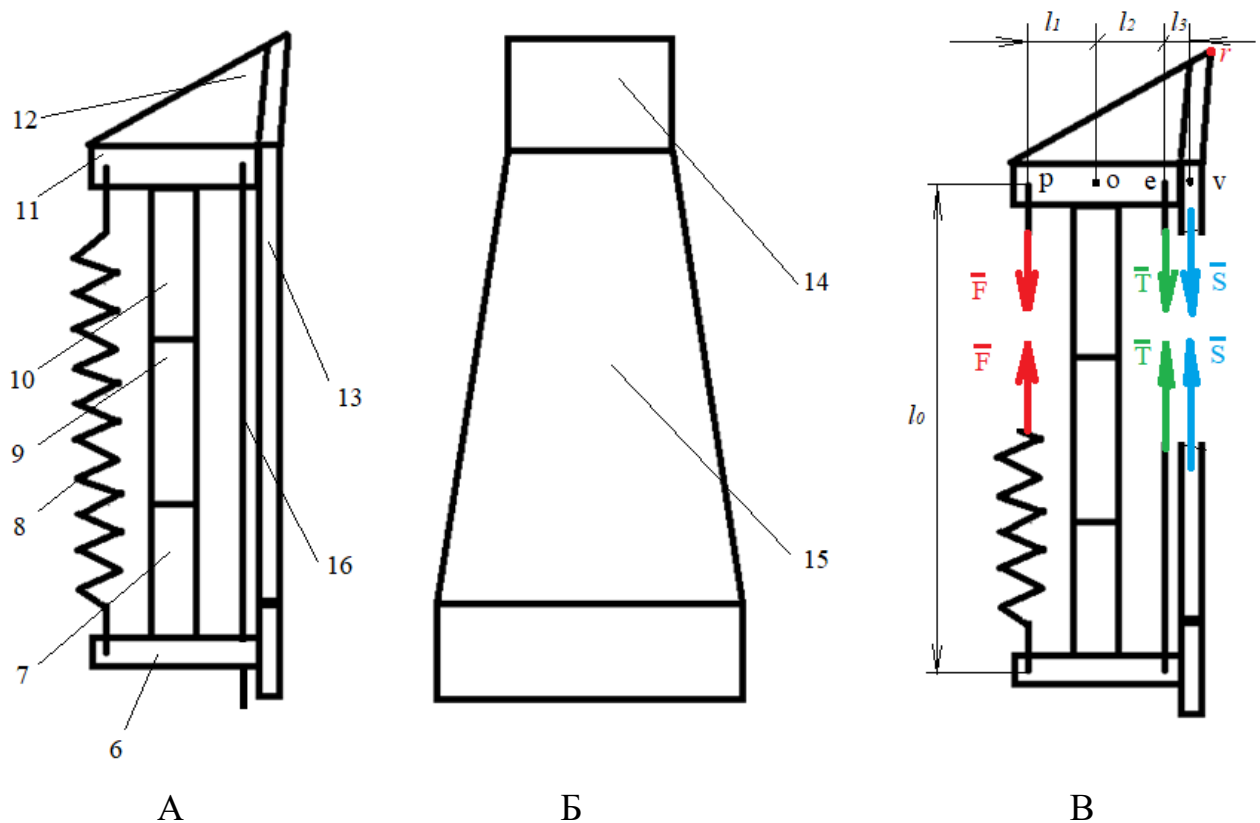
Схематичне зображення окремого пальця захвату та розрахункової схеми [28]: А – вид з боку на окремий палець захвату; Б – вид з переду на палець захвату; В – розрахункова схема для будови математичної моделі.
